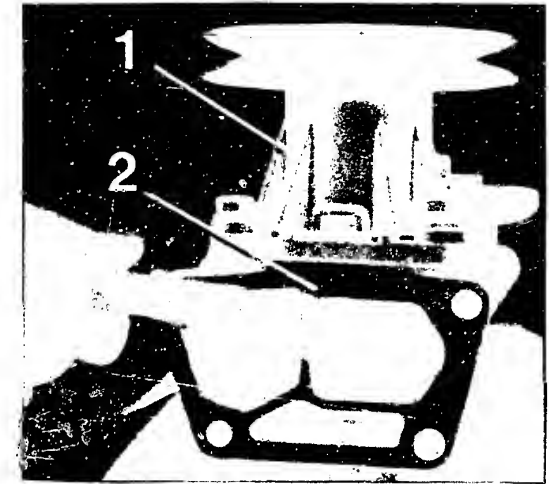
Motoren 1300 und 1500: Der Pumpendeckel (1) und das Pumpengehäuse (2) der Wasserpumpe sind zusammengeschrubt und können zerlegt werden. Das mit der Blattlehre zu messende Spiel zwischen Schaufelrad und Gehäuse muss 0,8...1,3mm betragen.
